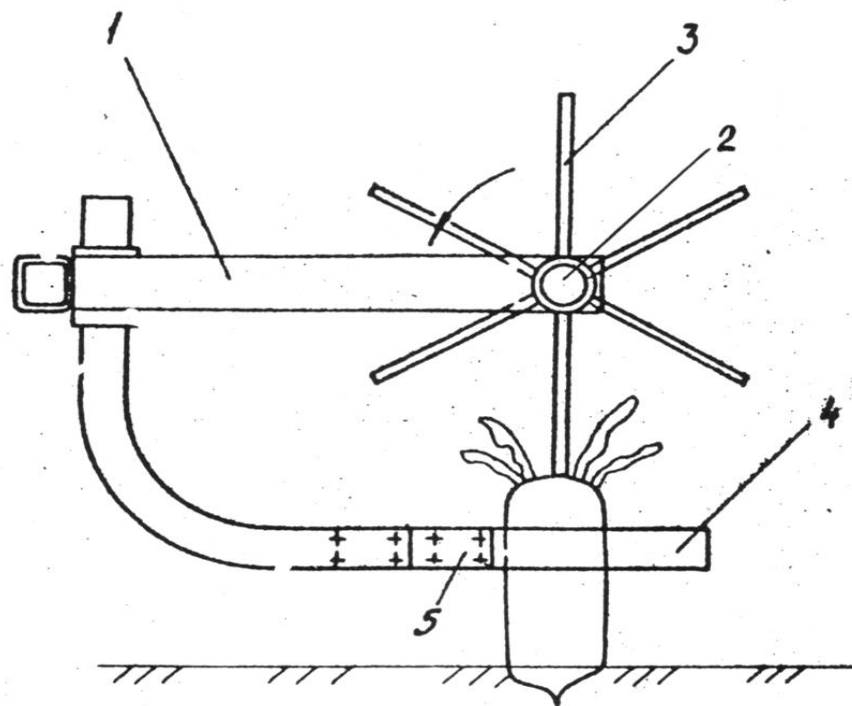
Схема очисника коренеплодів [12]: 1- рама; 2- вал;
